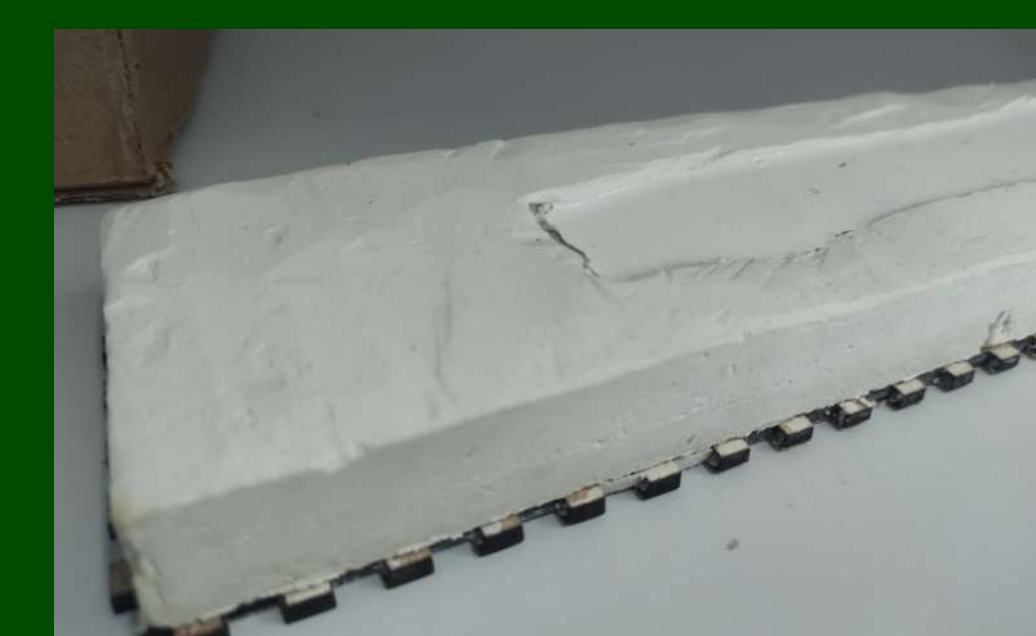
Molde de gesso com o silicone; Fonte: Autores.
